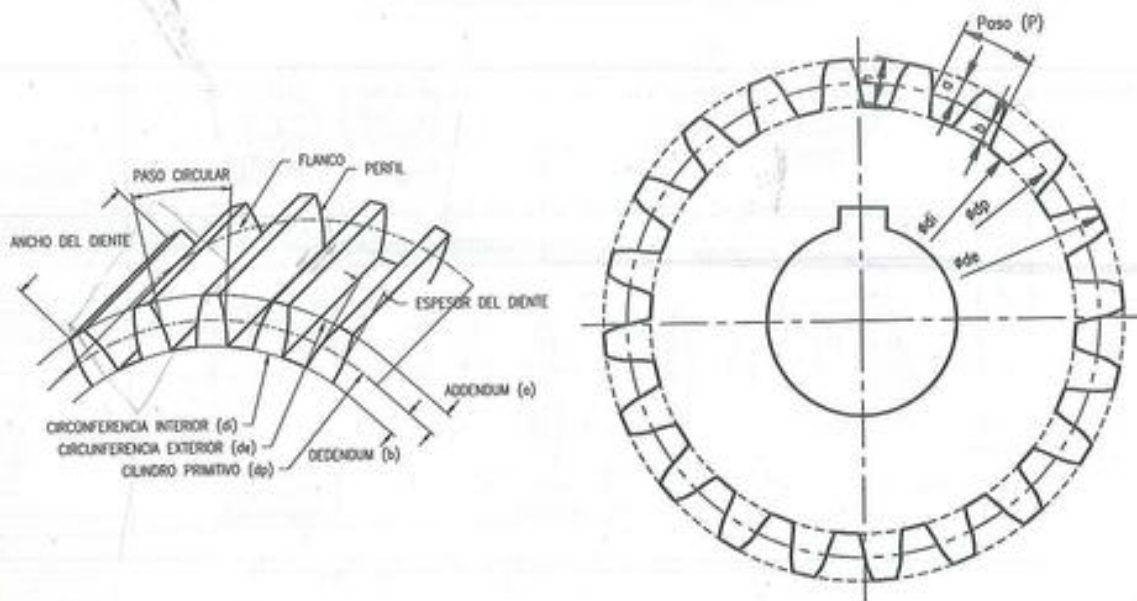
Engranajes cilíndricos. Definiciones.
